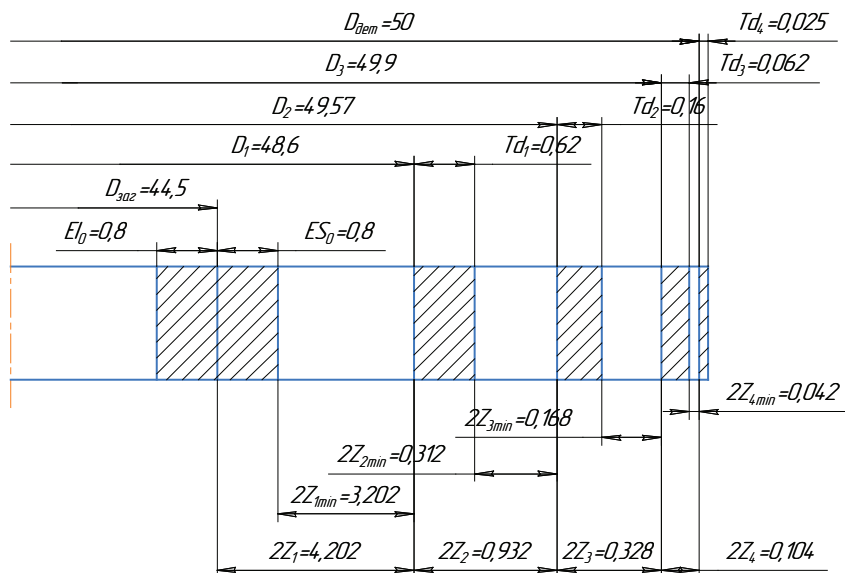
Схема распределения припусков для внутренней 13-й поверхности детали
